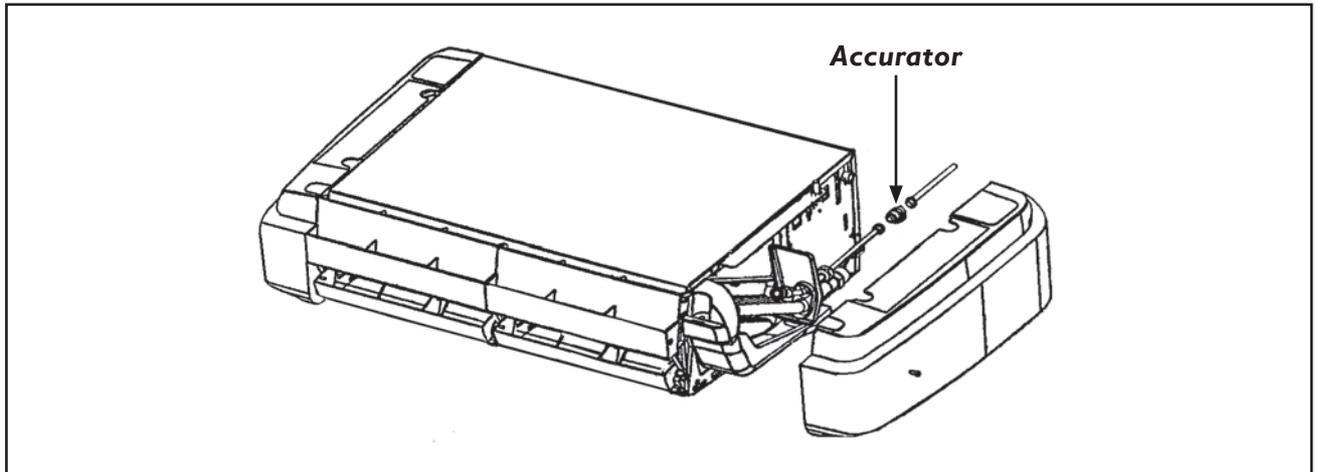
INSTALAÇÃO DO KIT SISTEMA DE EXPANSÃO (ACCURATOR)
